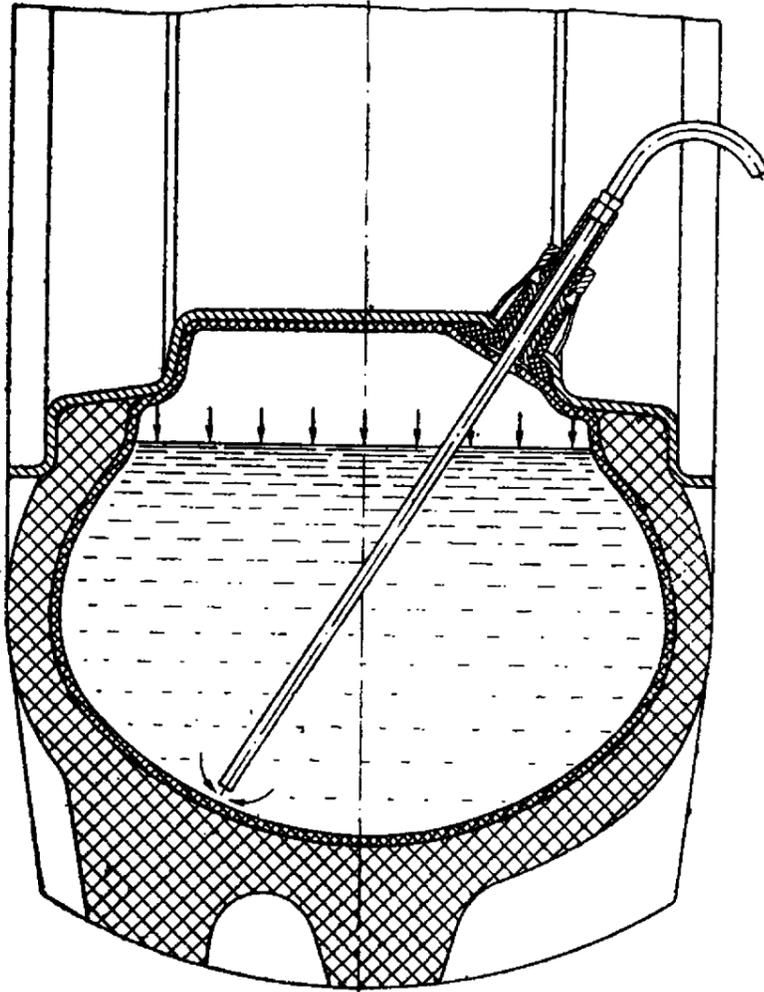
Приспособление для удаления воды из камеры без разборки колеса.
